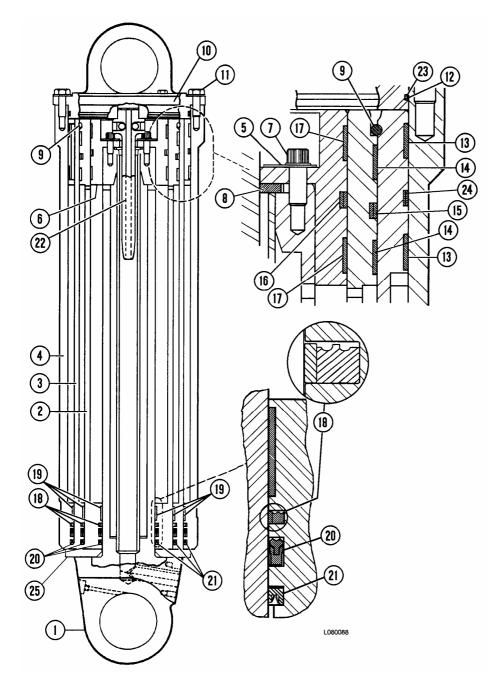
MONTAJE INFERIOR DEL CILINDRO DE ELEVACION
